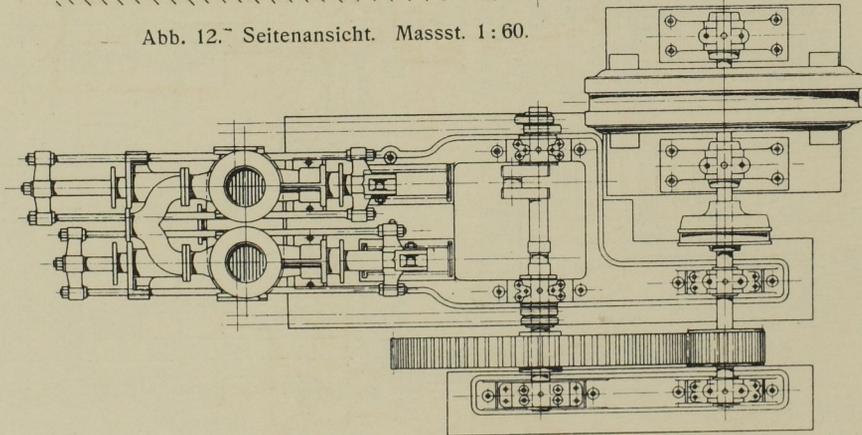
Grundriss der Pumpmaschine. Massst. 1:60.
